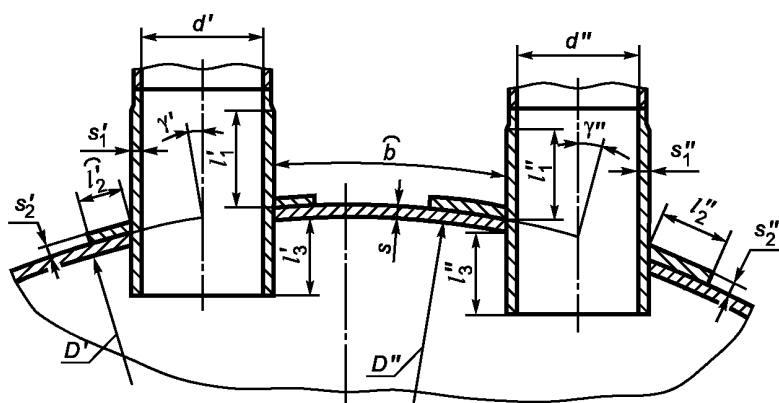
Укрепление отверстий торообразной вставкой или сварным кольцом
